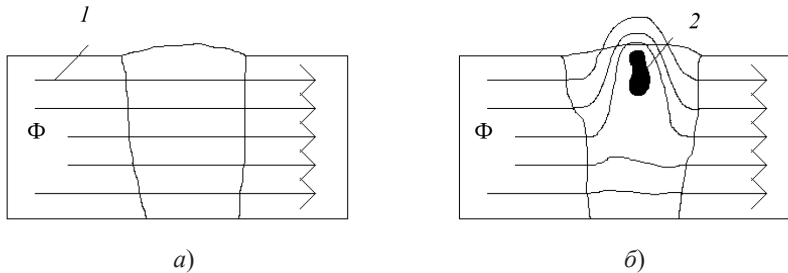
Схема прохождения магнитного потока в сварном соединении:
